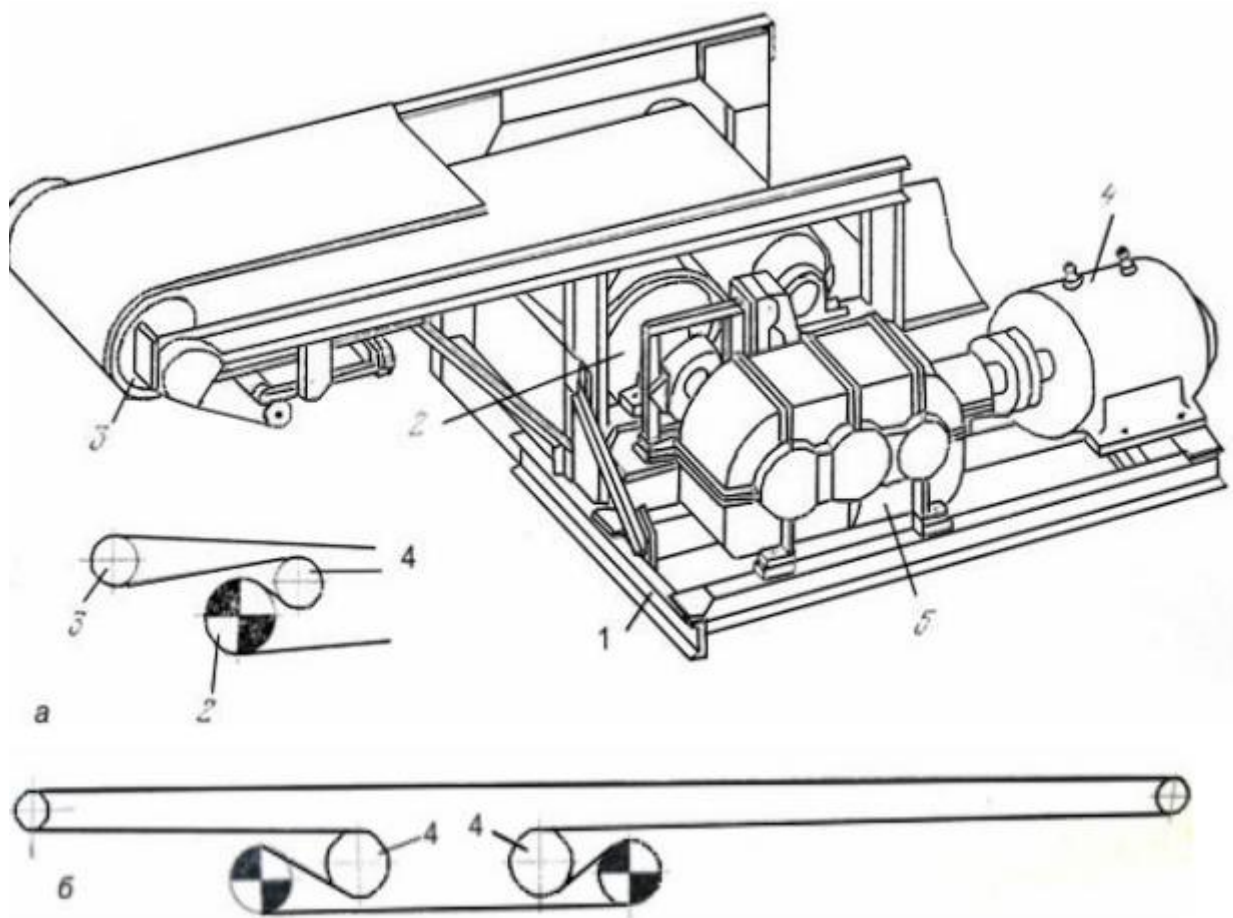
Конструкція та схеми приводу стрічкових конвеєрів. а) – з одним приводним барабаном; б) – з двома приводними барабанами.
